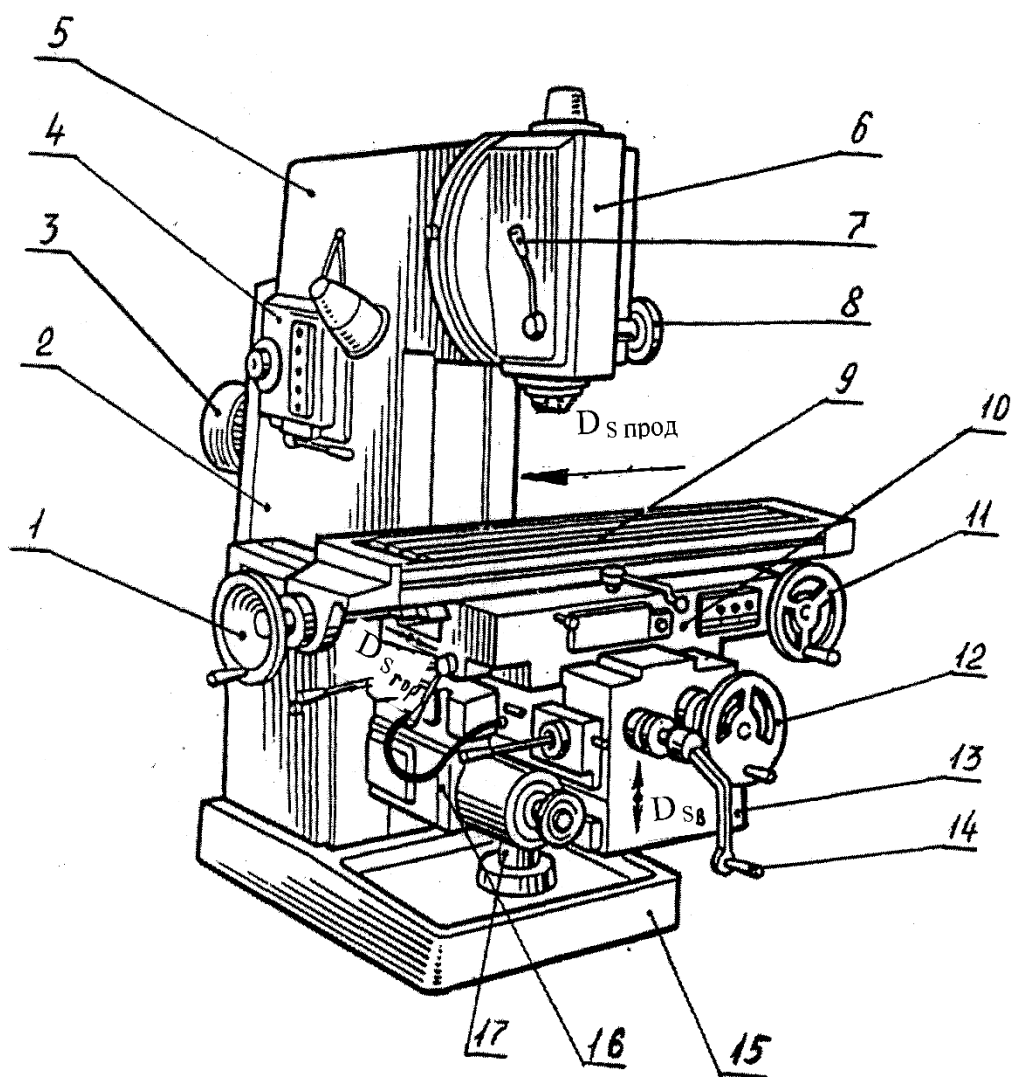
Консольный универсальный вертикально-фрезерный станок:
